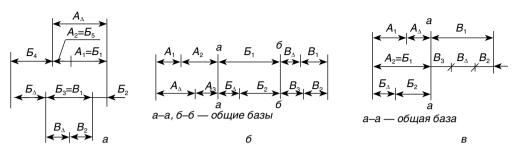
Размерные цепи с общими звеньями: а — размерные цепи с несколькими общими звеньями; б — размерные цепи с общей базой; в — комбинированная размерная цепь
